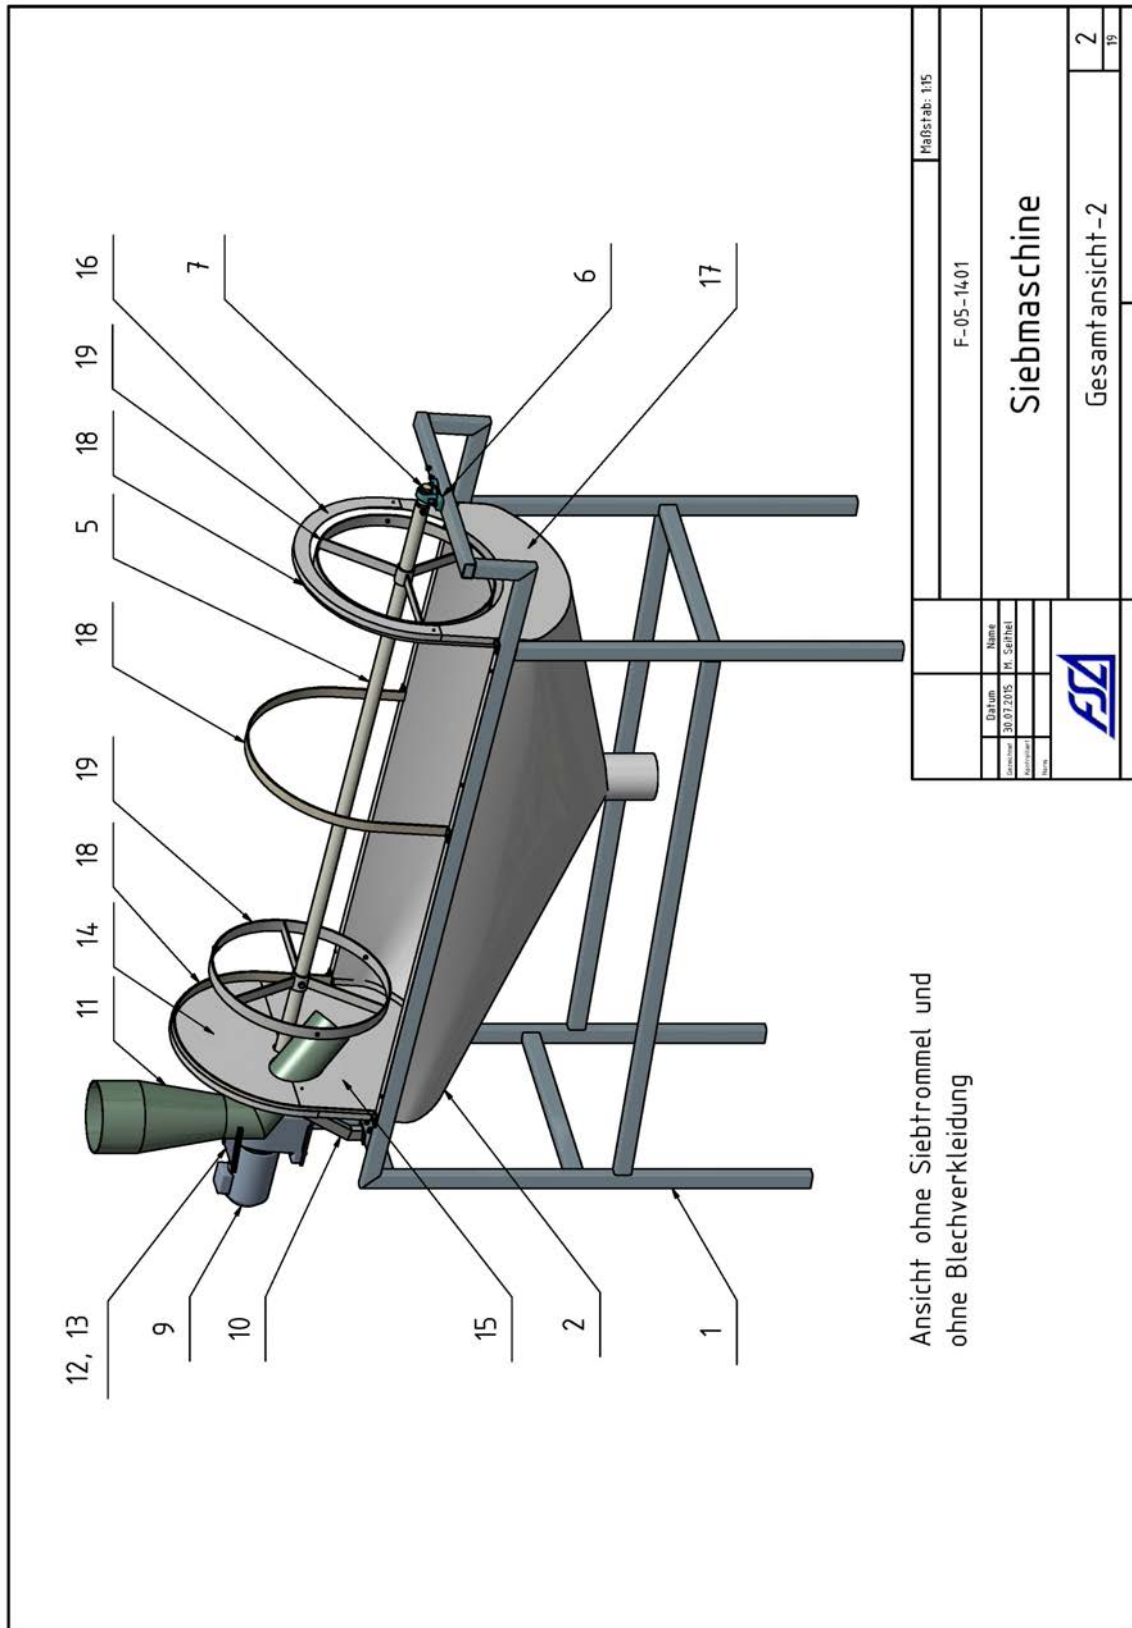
Konstruktionszeichnung zur Siebmaschine.
